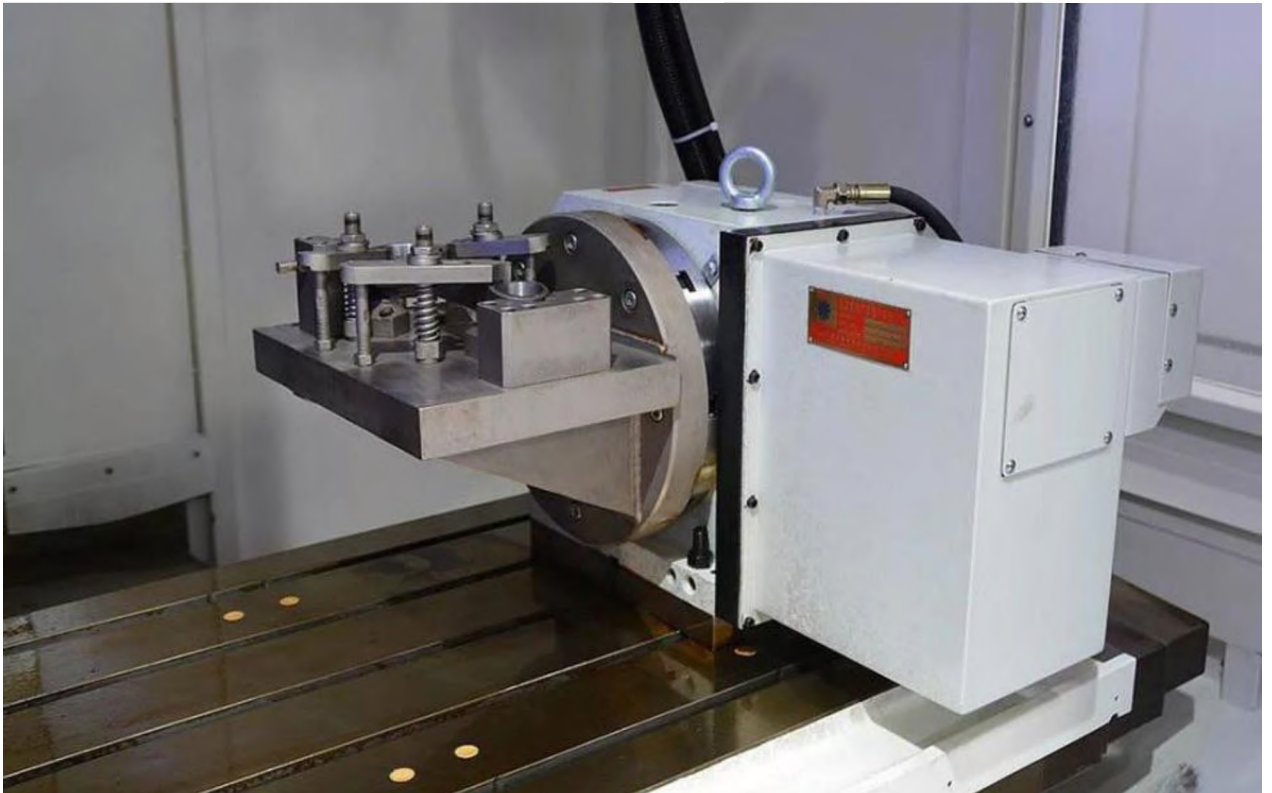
Стіл оброблювального центру з ЧПК CORMAK MILL1042
